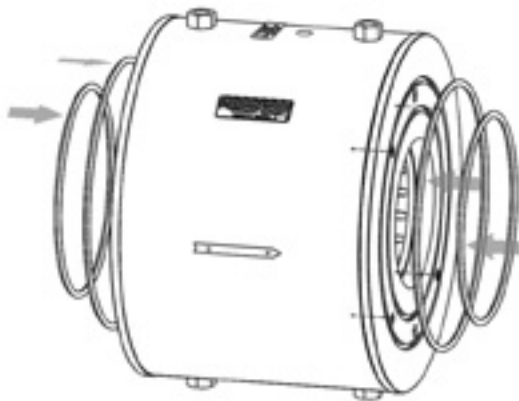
Bringen Sie die O-Ringe der Abdeckplatte wieder an.
